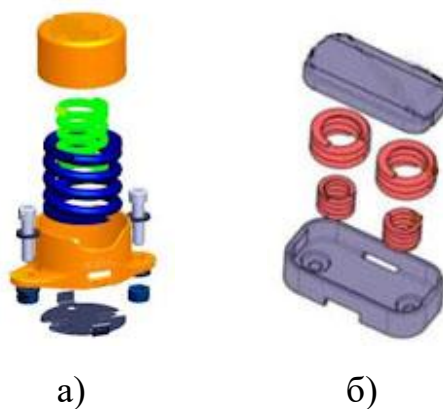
Конструкции боковых скользунов с винтовыми пружинами [142]:
